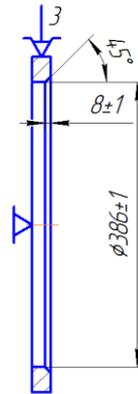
Эскиз базирования заготовки на 010 токарной операции.
